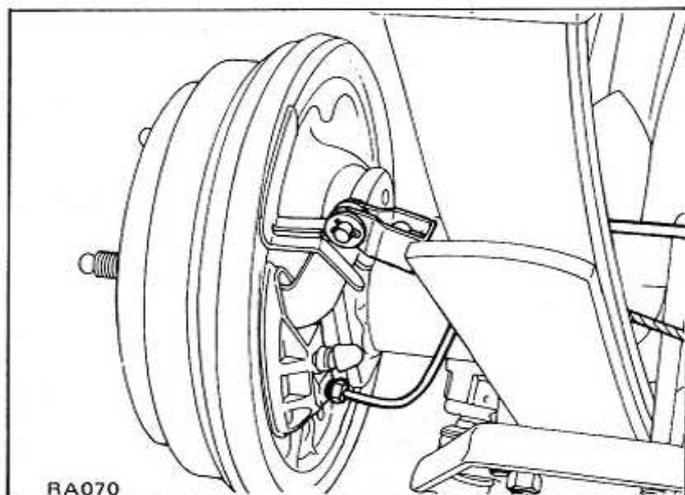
Dépose du câble de frein à main et du tuyau de liquide
